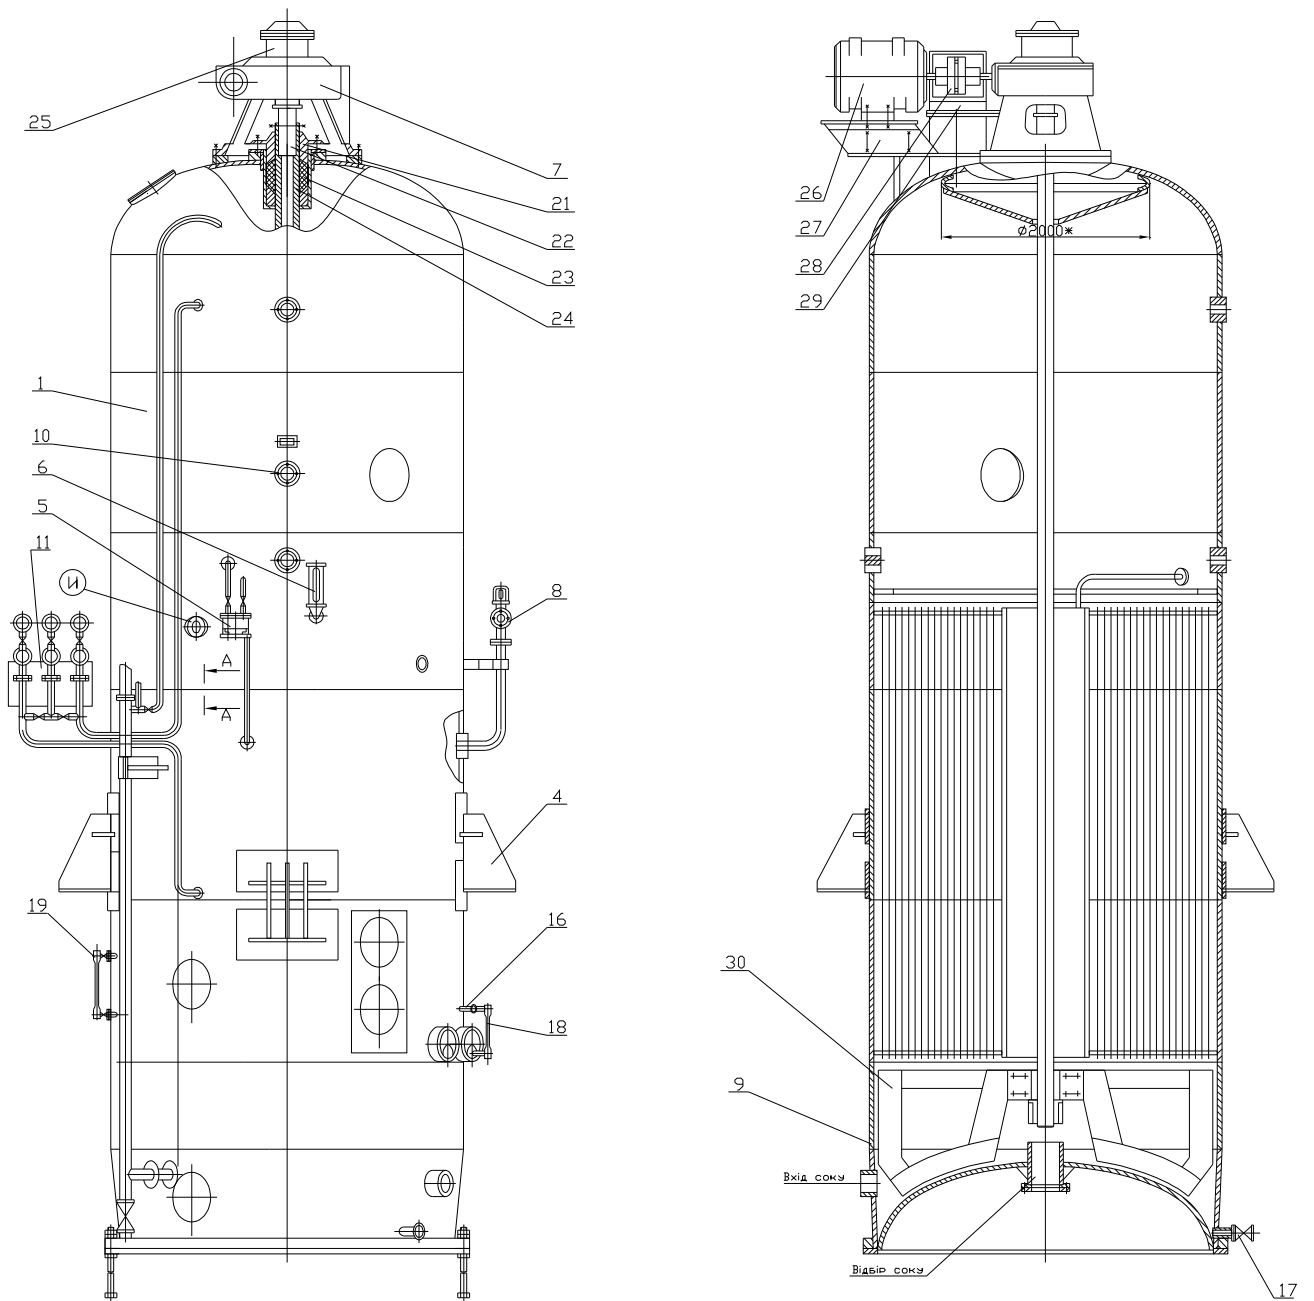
Будова випарного апарата площею нагріву: 1 – верхня частина корпусу; 2, 3 – камери парові; 4 – лапа опорна; 5 – маслянка; 6 – термометр; 7 – редуктор; 8 – клапан запобіжний; 9 – днище; 10 – вікно оглядове; 11 – щиток з манометрами; 12 – лаз; 16 – запірний пристрій; 17 – вентиль; 18, 19 – трубки; 20 – мішалка; 21 – фланець; 22 – стакан; 23 – ущільнення; 24 – вал; 25 – кришка; 26 – електродвигун; 27 – рама; 28 – муфта; 29 – щиток муфти; 30 - мішалка
